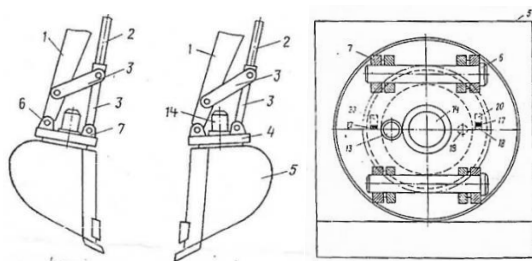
Предлагаемая конструкция рабочего оборудования одноковшового экскаватора
